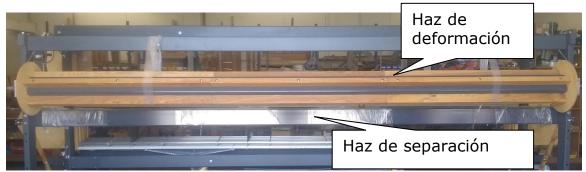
Viga de urdimbre y separación be a m en telar de acero
